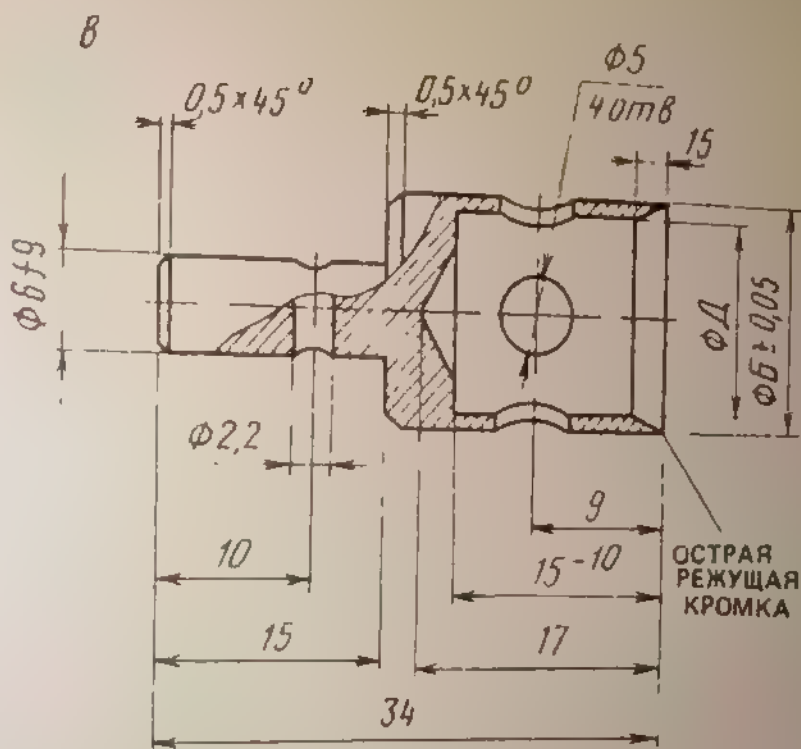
Процесс изготовления резиновых изделий и ножи для их вырезания
